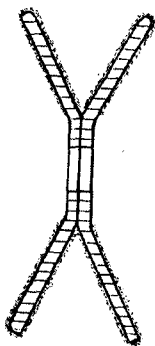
Абразивный инструмент из двух тарельчатых пружин, образующих X-образный профиль.
